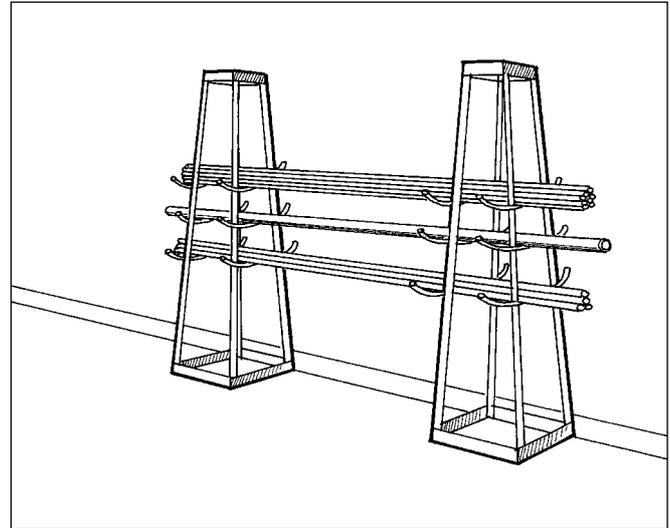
Dispositif d'entreposage horizontal de barres. Peut être utilisé seul pour le stockage de pièces courtes, ou par deux, en les alignant, pour stocker des pièces plus longues
